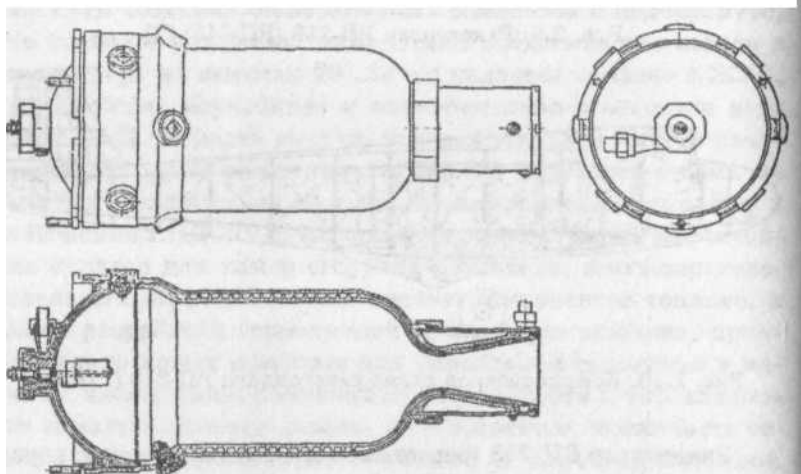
Жидкостный ракетный двигатель ОРМ-70 [12]
